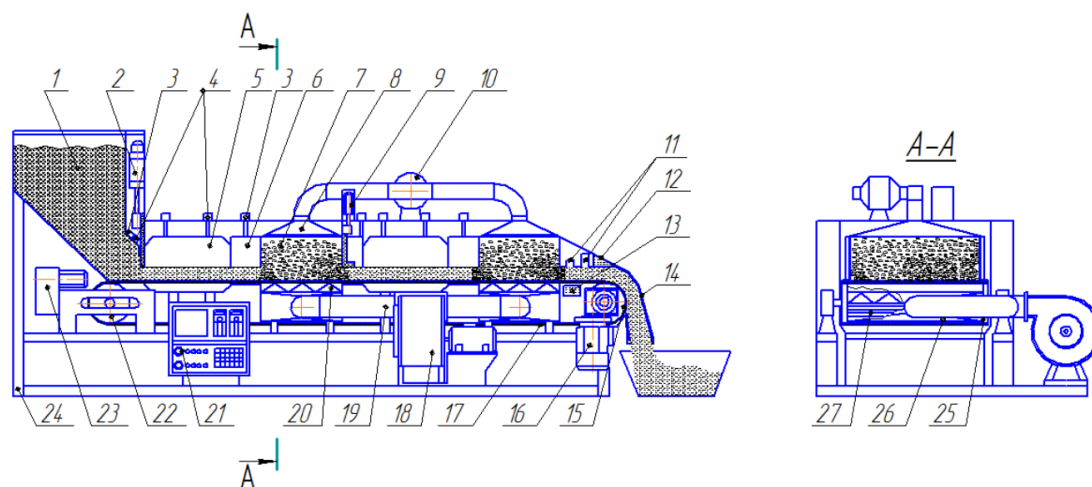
Схема НВЧ-установки для сушіння та мікрохвильової обробки зерна
